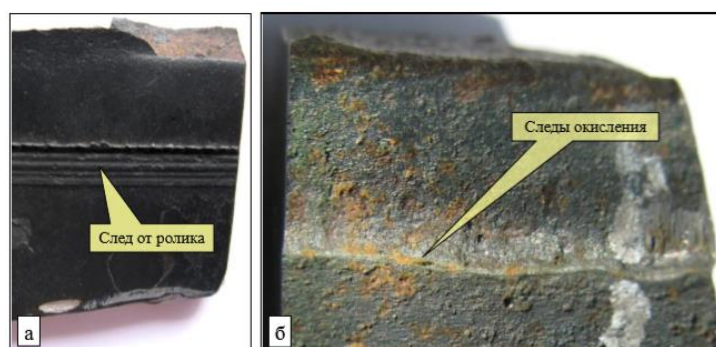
Дефекты на поверхности трубы и сварном соединении:
